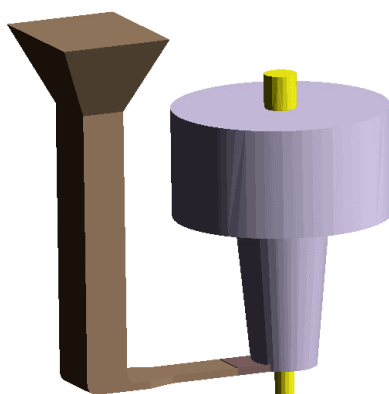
Vista isométrica do corpo de prova em três dimensões com sistema de enchimento.
